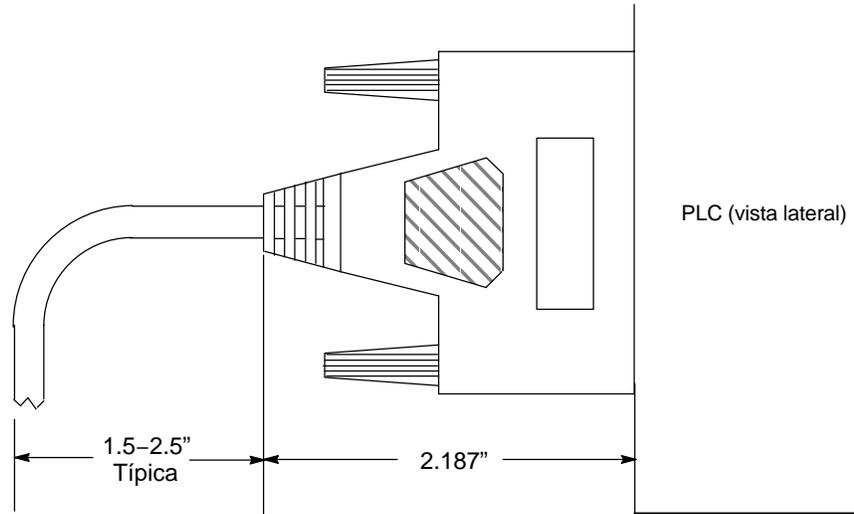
Dimensiones de profundidad del conector en el frontal del PLC
